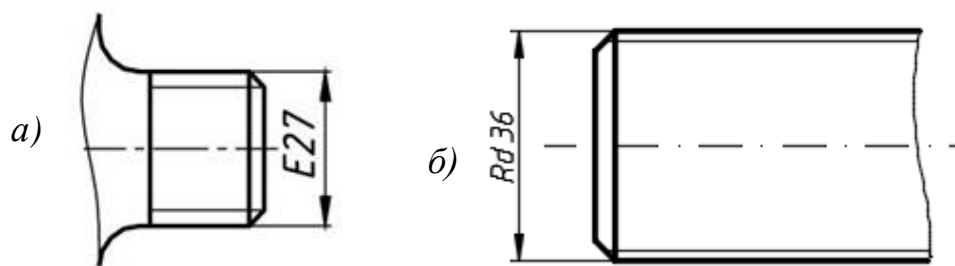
Обозначение круглой резьбы на чертежах:
